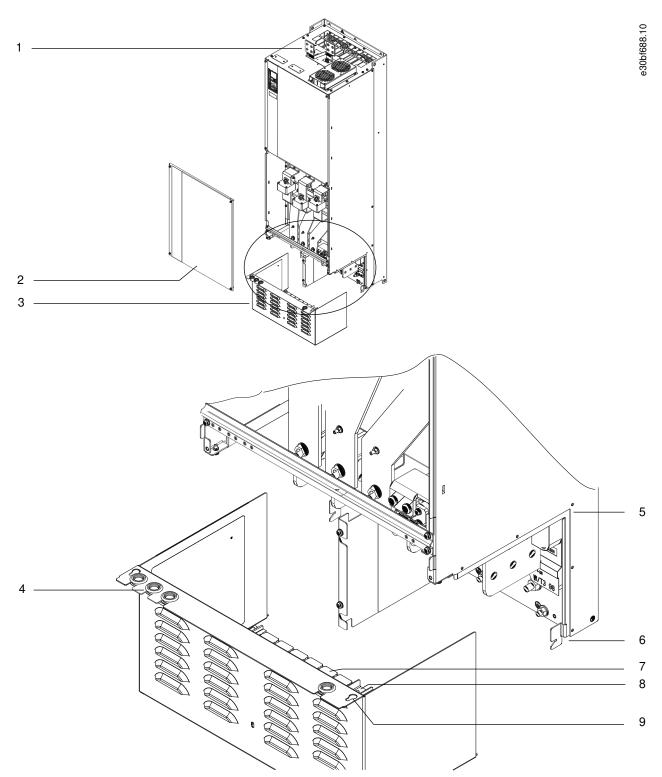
Assemblage de la plaque d'entrée des câbles et de la protection borniers
